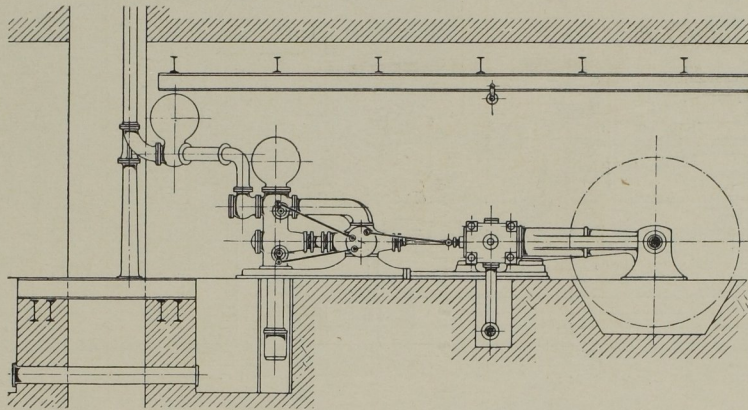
Schnitt durch den Maschinenraum und Seitenansicht der Maschine. Massst. 1:64.
